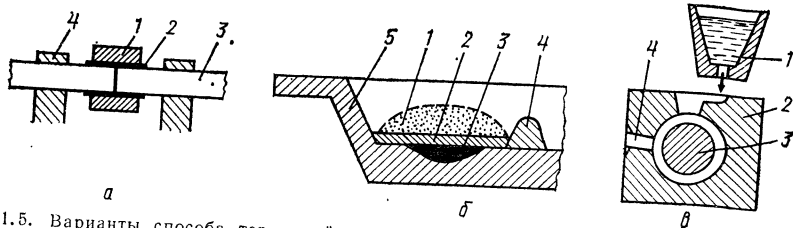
Варианты способа термитной сварки плавлением:
